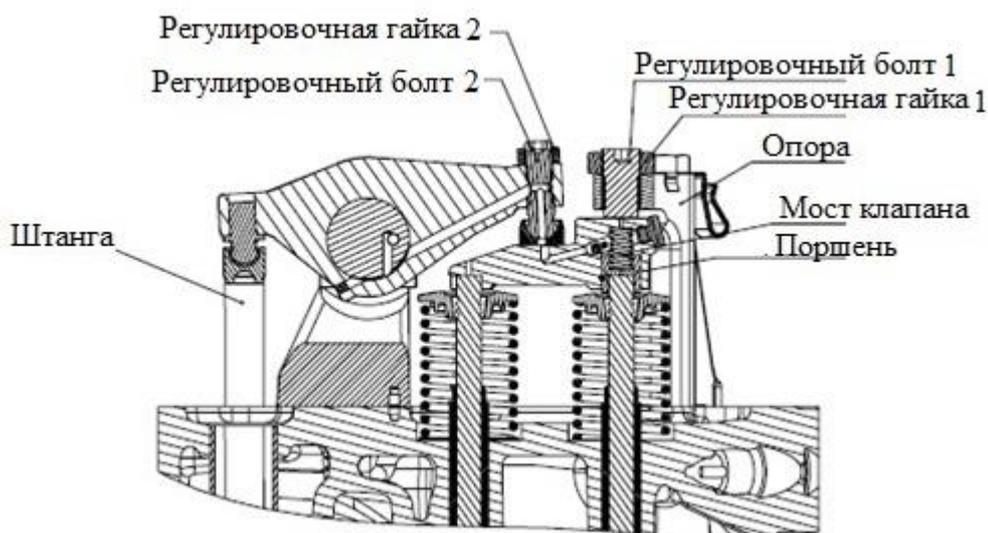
Регулировка зазора выпускного клапана с тормозным устройством WEVB
